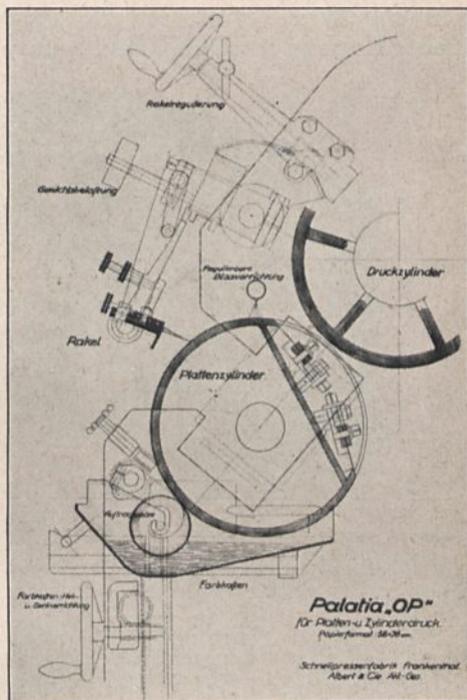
Schnitt durch das Druckwerk einer „Palatia-OP“-Tiefdruckmaschine in der Einstellung für Plattendruck
